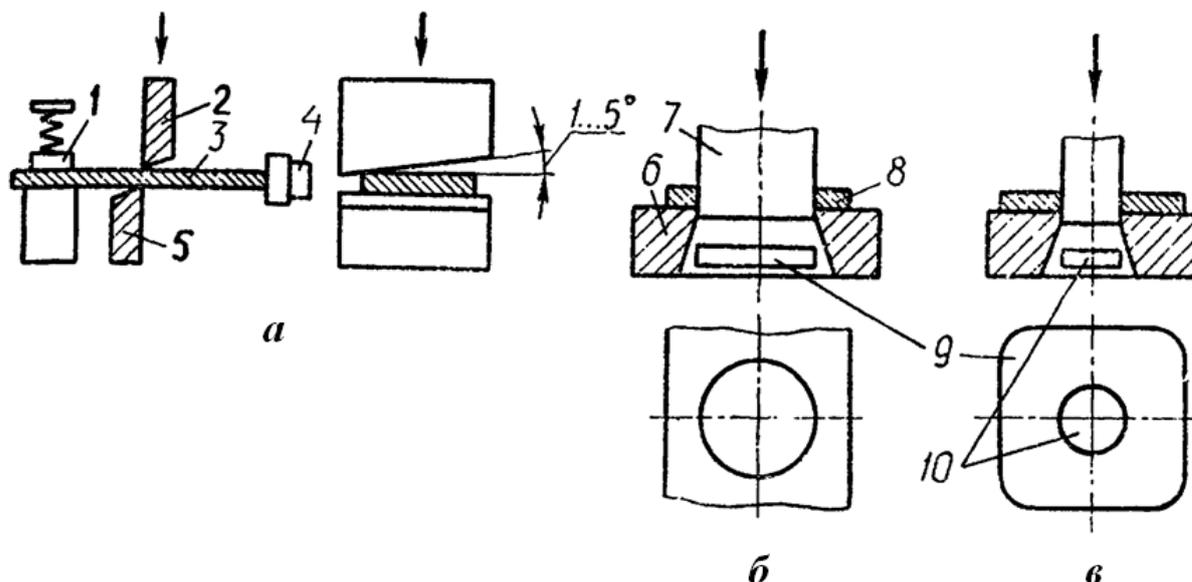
Разделительные операции листовой штамповки: *а* – отрезка; *б* – вырубка; *в* – пробивка
